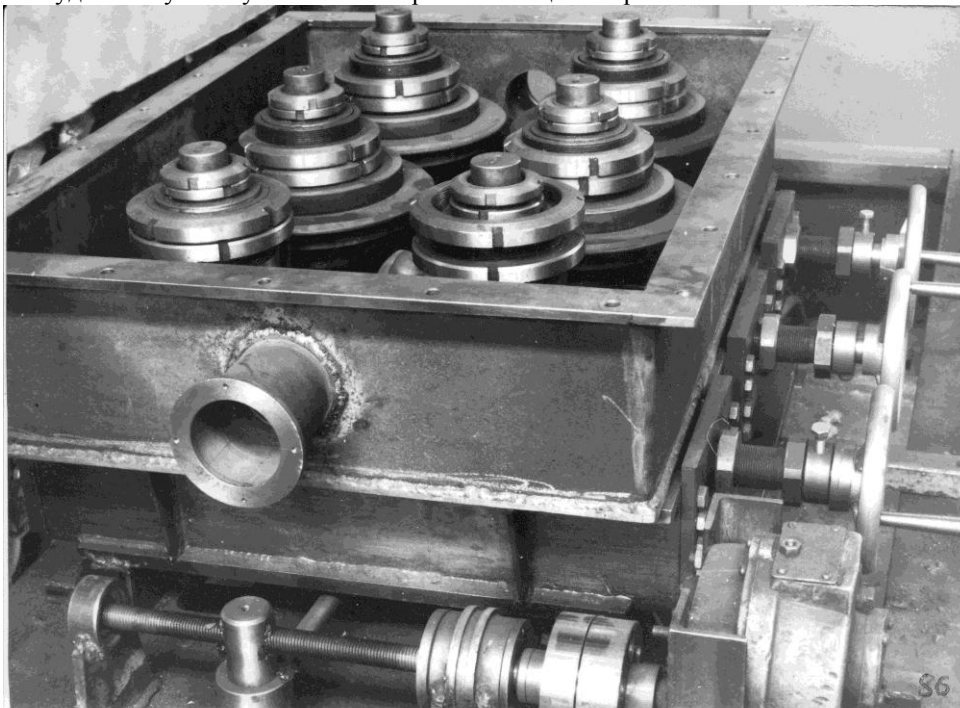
Внешний вид опорно-сварочного узла ТЭСА АДС
